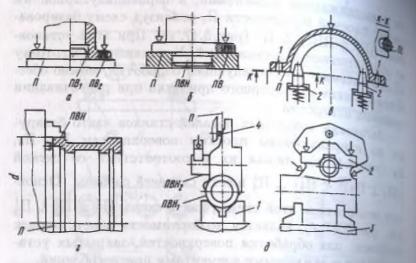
Схемы базирования заготовок фланцевых корпусных деталей
